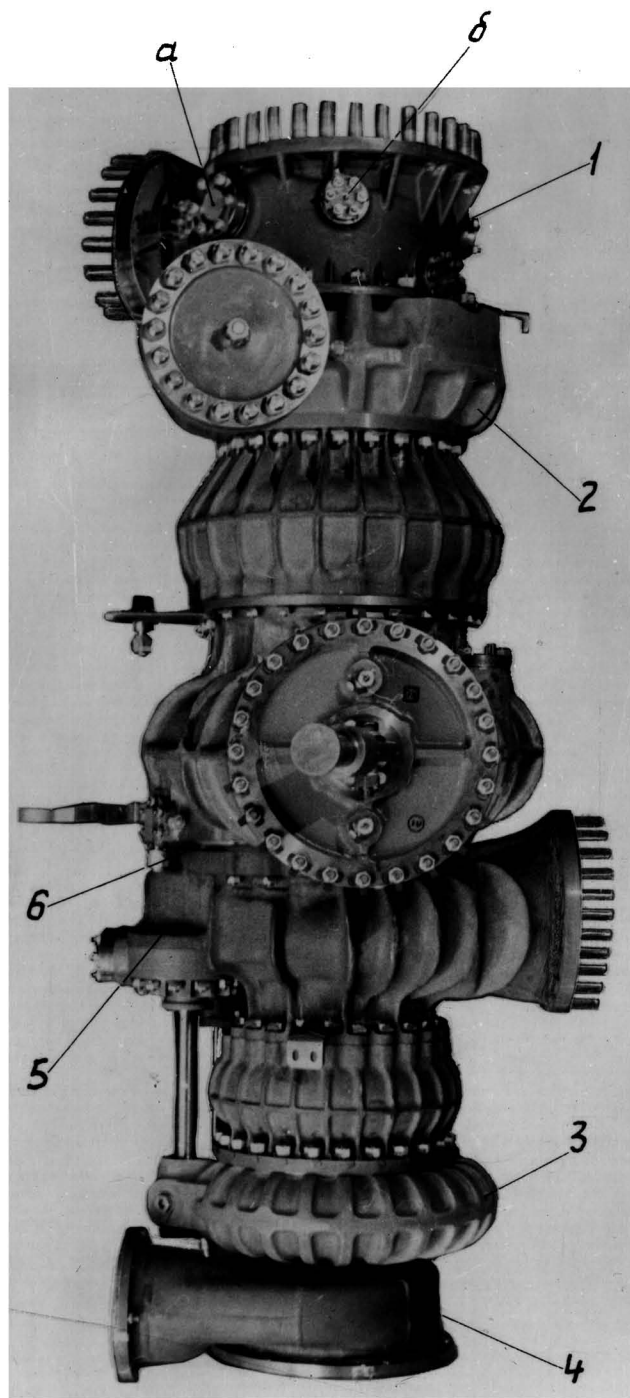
Общий вид турбонасосного агрегата 33.290.000-1:
